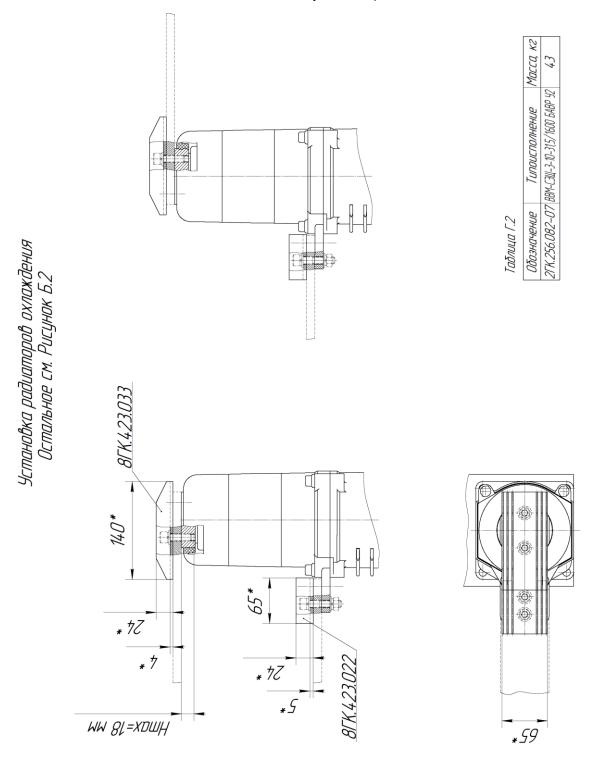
Габаритные, присоединительные и установочные размеры выключателя типа BBM-СЭЩ-3-10-31,5/1600 БАВР У2
